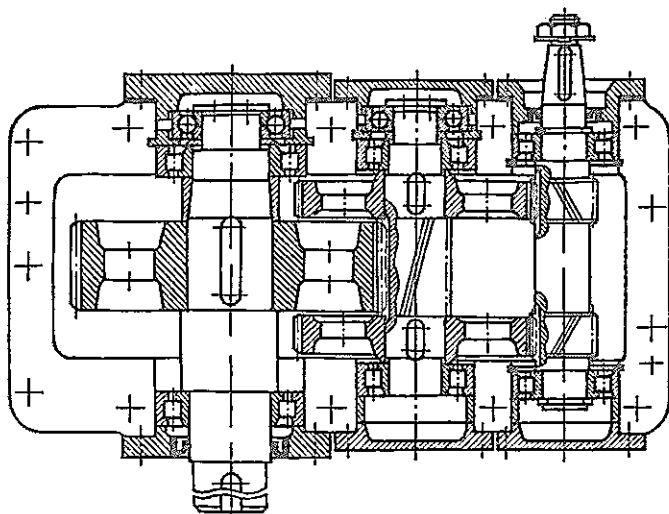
Цилиндрический двухступенчатый редуктор с раздвоенной быстроходной ступенью и раздельными опорами валов для восприятия радиальной и осевой нагрузок
